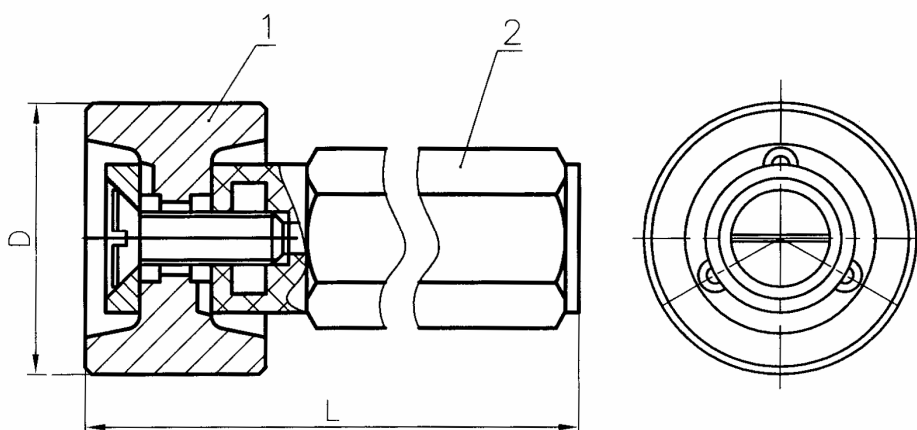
Калибр-пробка штампованный с насадкой:
